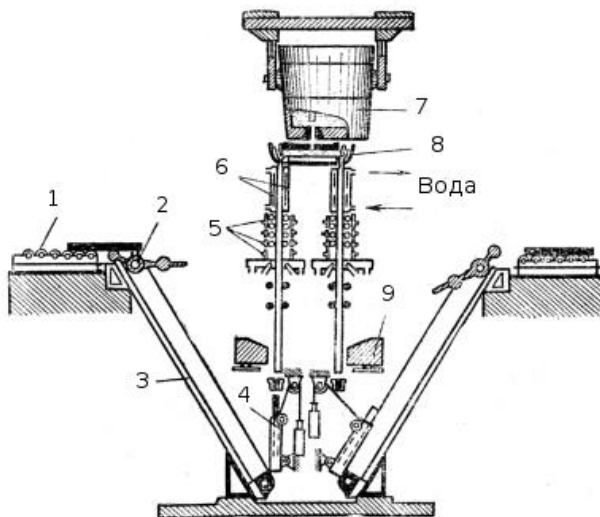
Принципиальная схема и установка для непрерывной разливки стали с двумя машинами:
